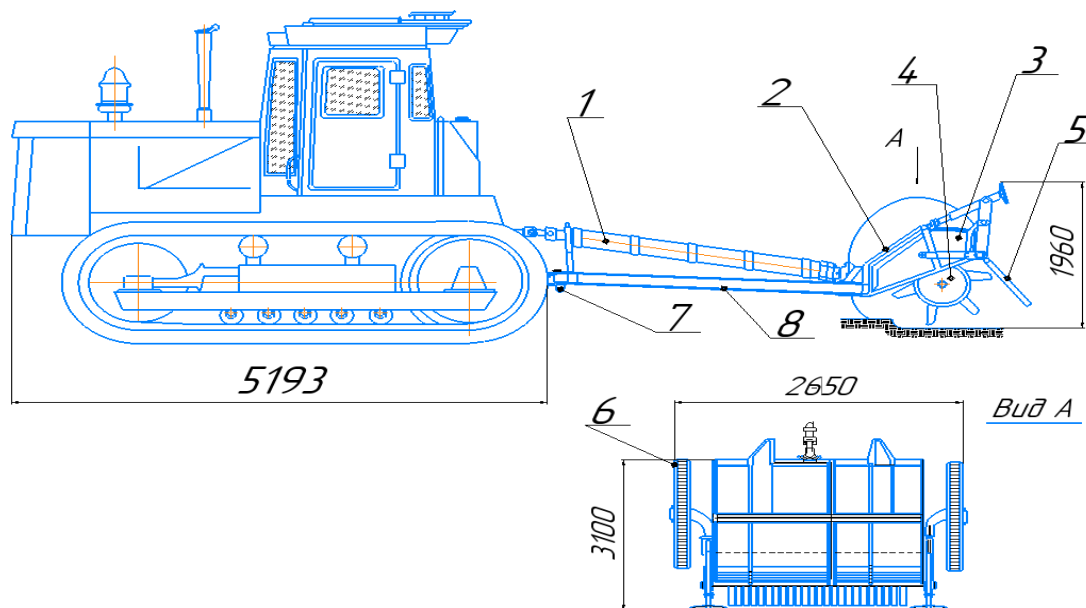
Общий вид агрегата для проведения фрезерования почвы
